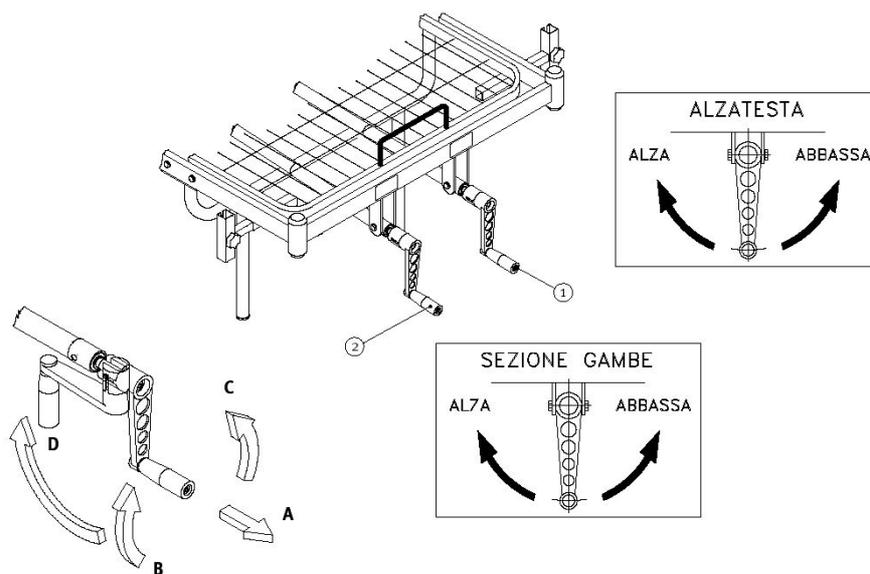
Regolazione delle sezioni alzatesta e gambe Art. A 5112 – A 5132
